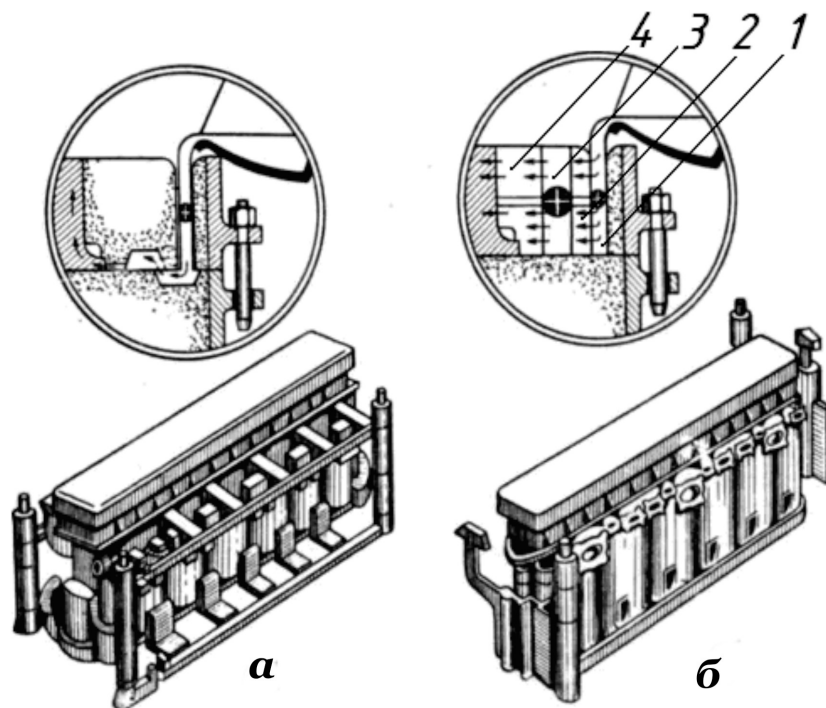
Схема заливки форм блоков цилиндров двигателей жидкостного охлаждения: а – сифонный метод, при котором получается отливка блока цилиндра двигателя массой 200 кг; б – вертикально-целевым стояком, при котором та же отливка получается 120 кг в черновом весе; 1 – стояк; 2 – целевой промежуточный канал; 3 – вертикальный распределительный канал; 4 – целевой питатель
